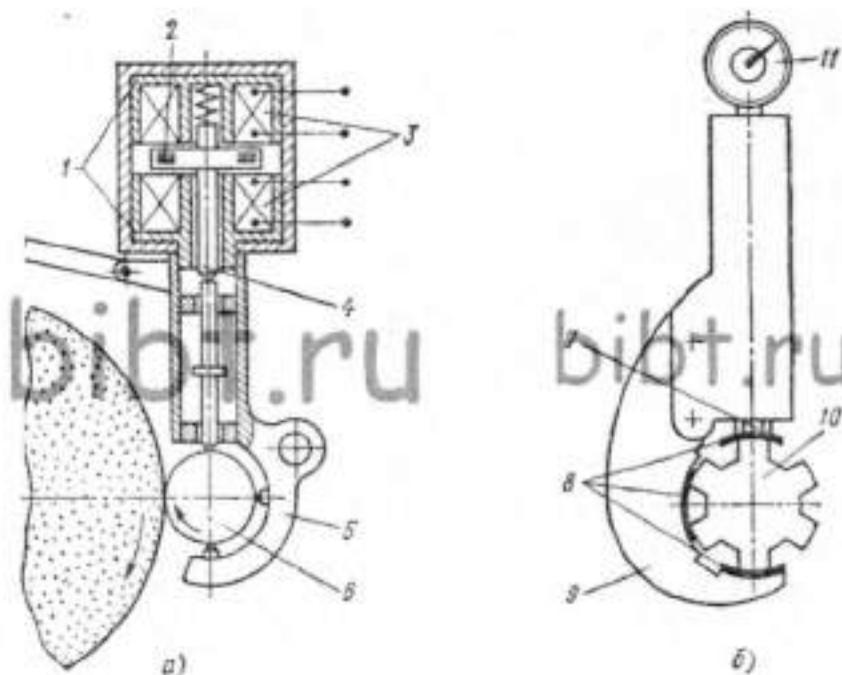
Устройства для активного контроля на круглошлифовальных станках:
